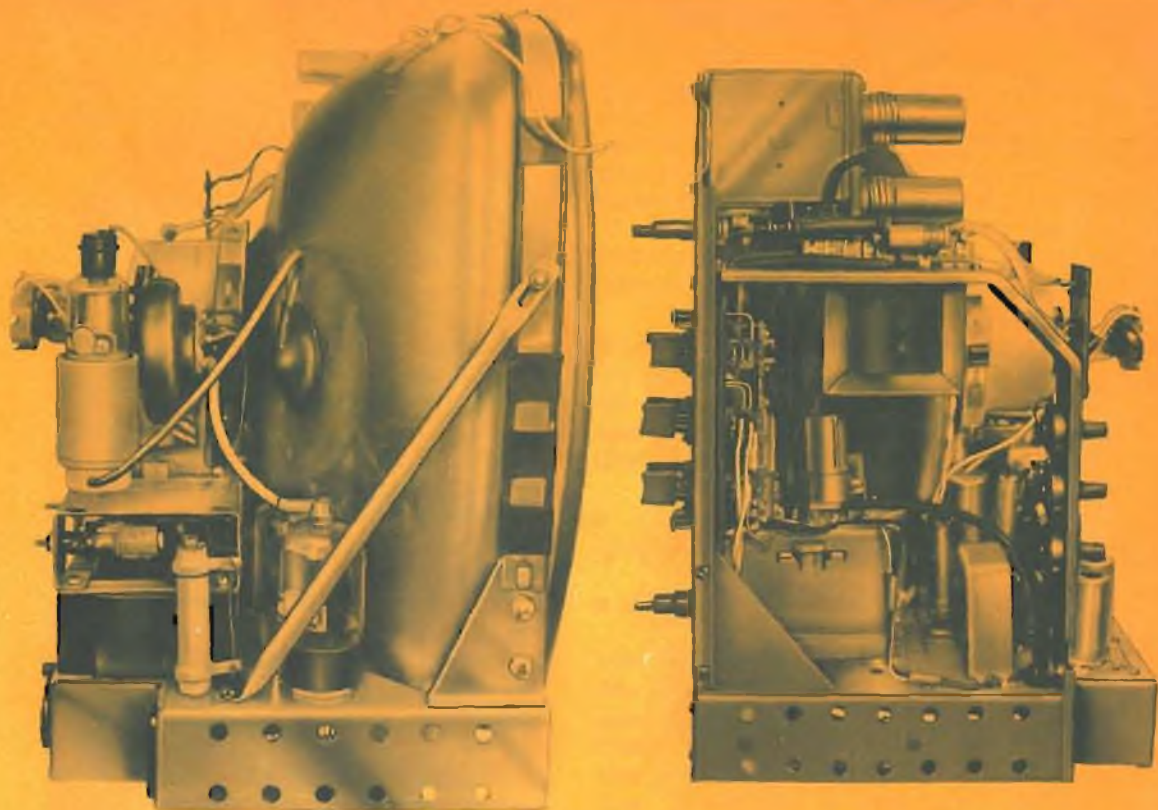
Montaggio della fascia per il fissaggio del tubo.
